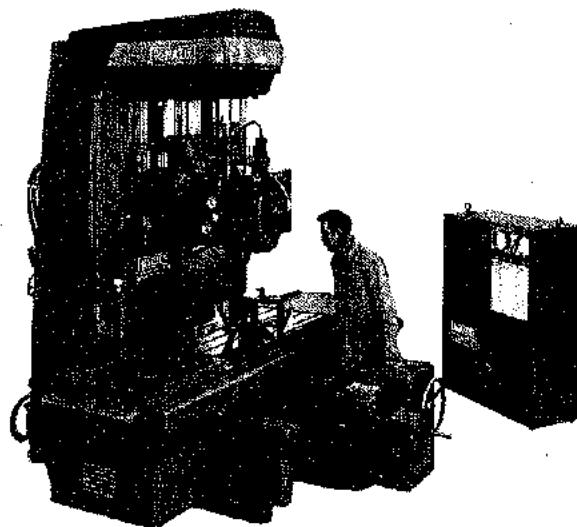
Sistema de control numérico típico, aplicado a una máquina de precisión para el mandrinado de montajes (Fosdick Machine Tool Co.)
